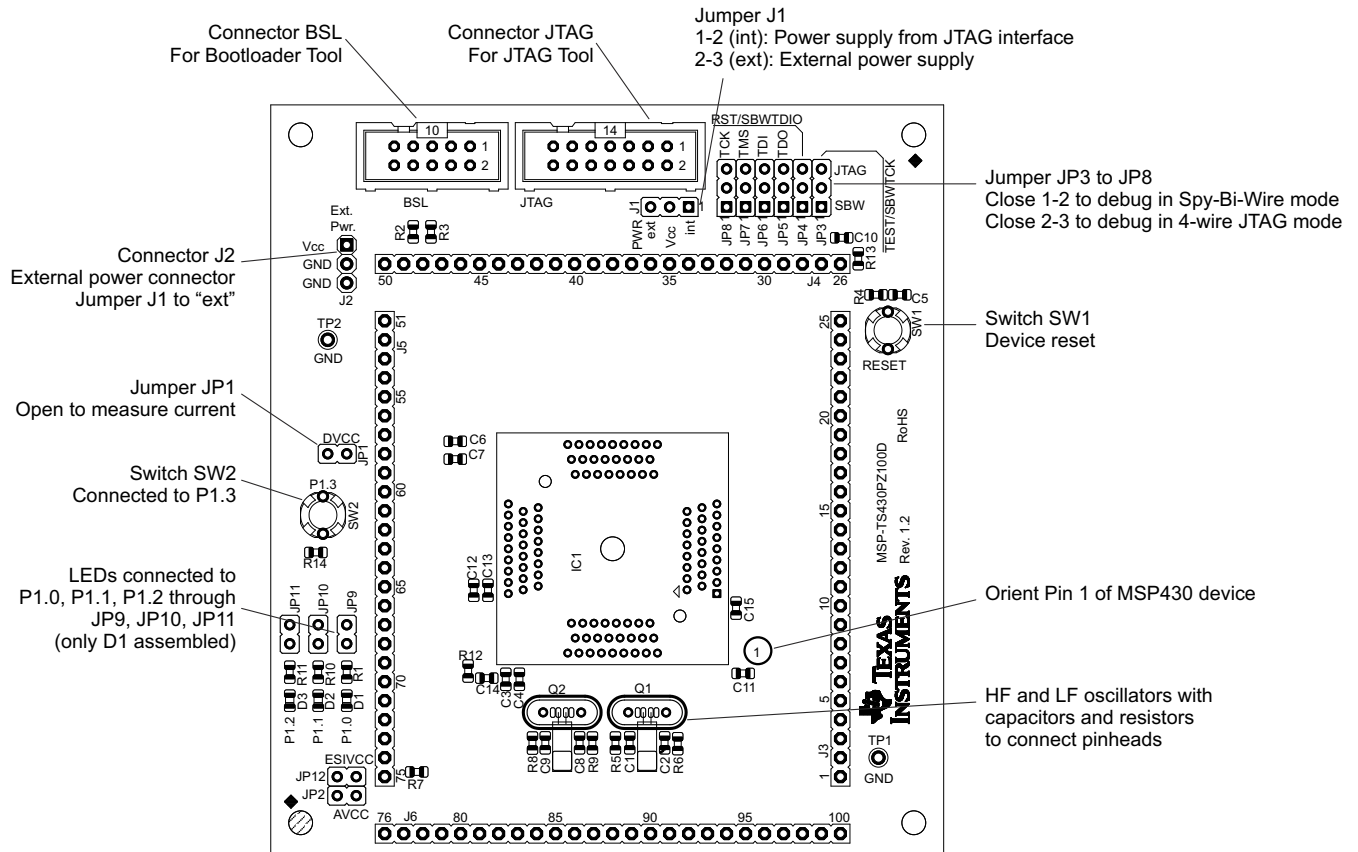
MSP-TS430PZ1000 目标插座模块, PCB
